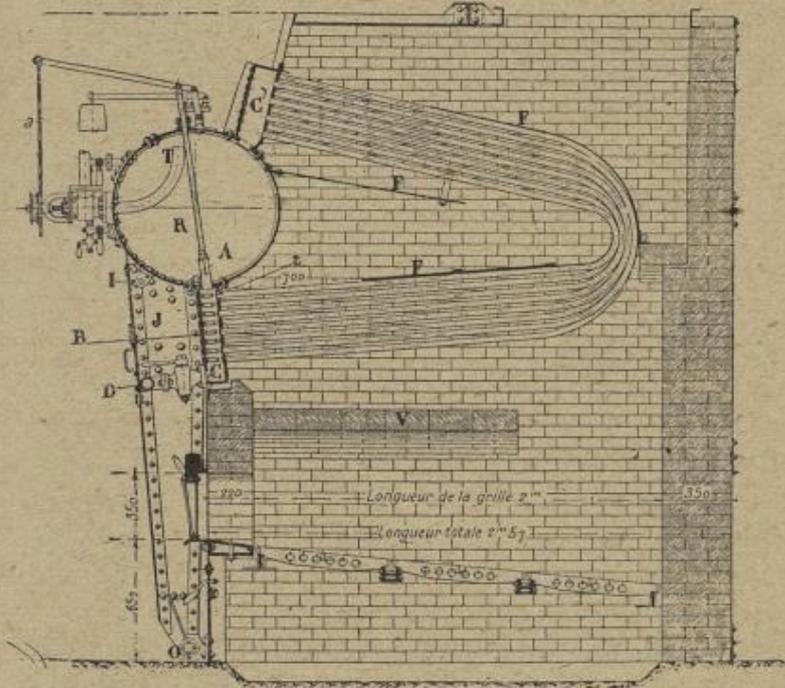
Coupe longitudinale de la chaudière Solignac-Grille.
